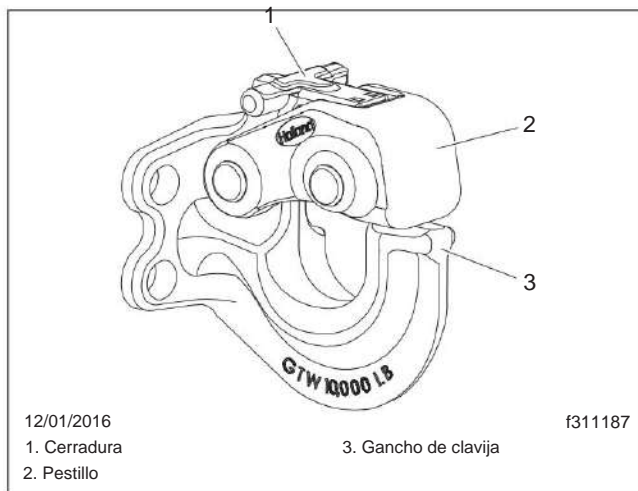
, Acoplamiento de remolque Holland con FastLatch
